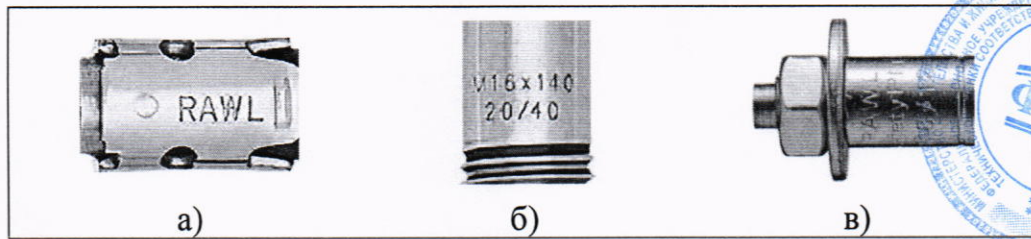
Маркировка анкеров RAWLPLUG типа R-НРТII и R-SPL
